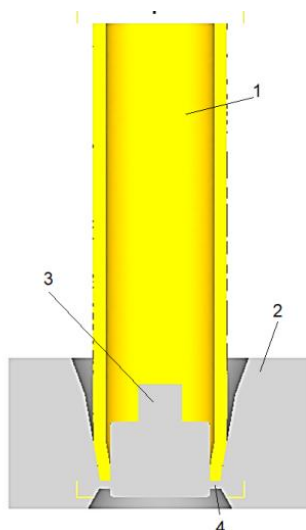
Чертеж конической волоки и короткой цилиндрической оправки
